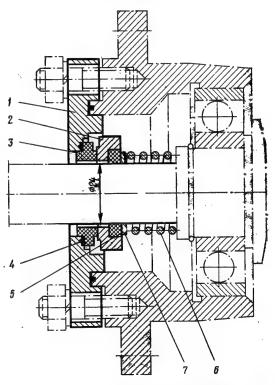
Сальник пружинный уплотнения вала с кольцами трения (компрессор ФВ6):
